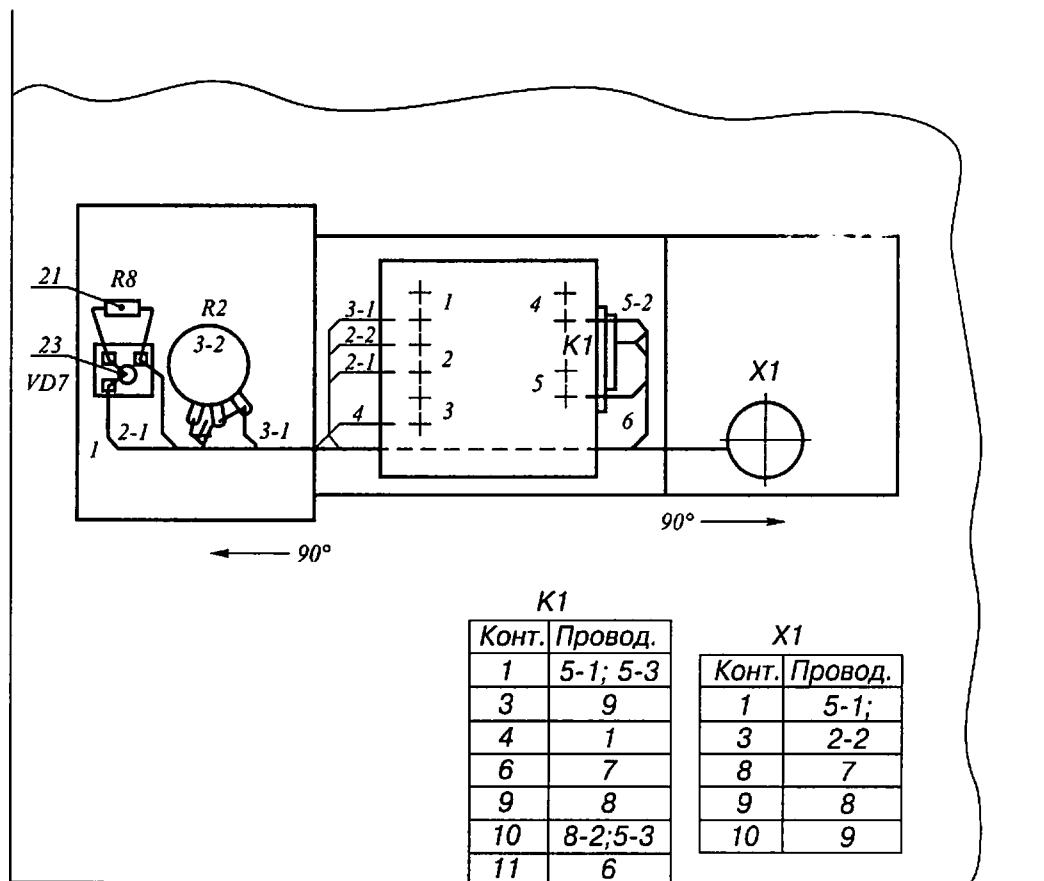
Електромонтажний кресленик (фрагмент)
